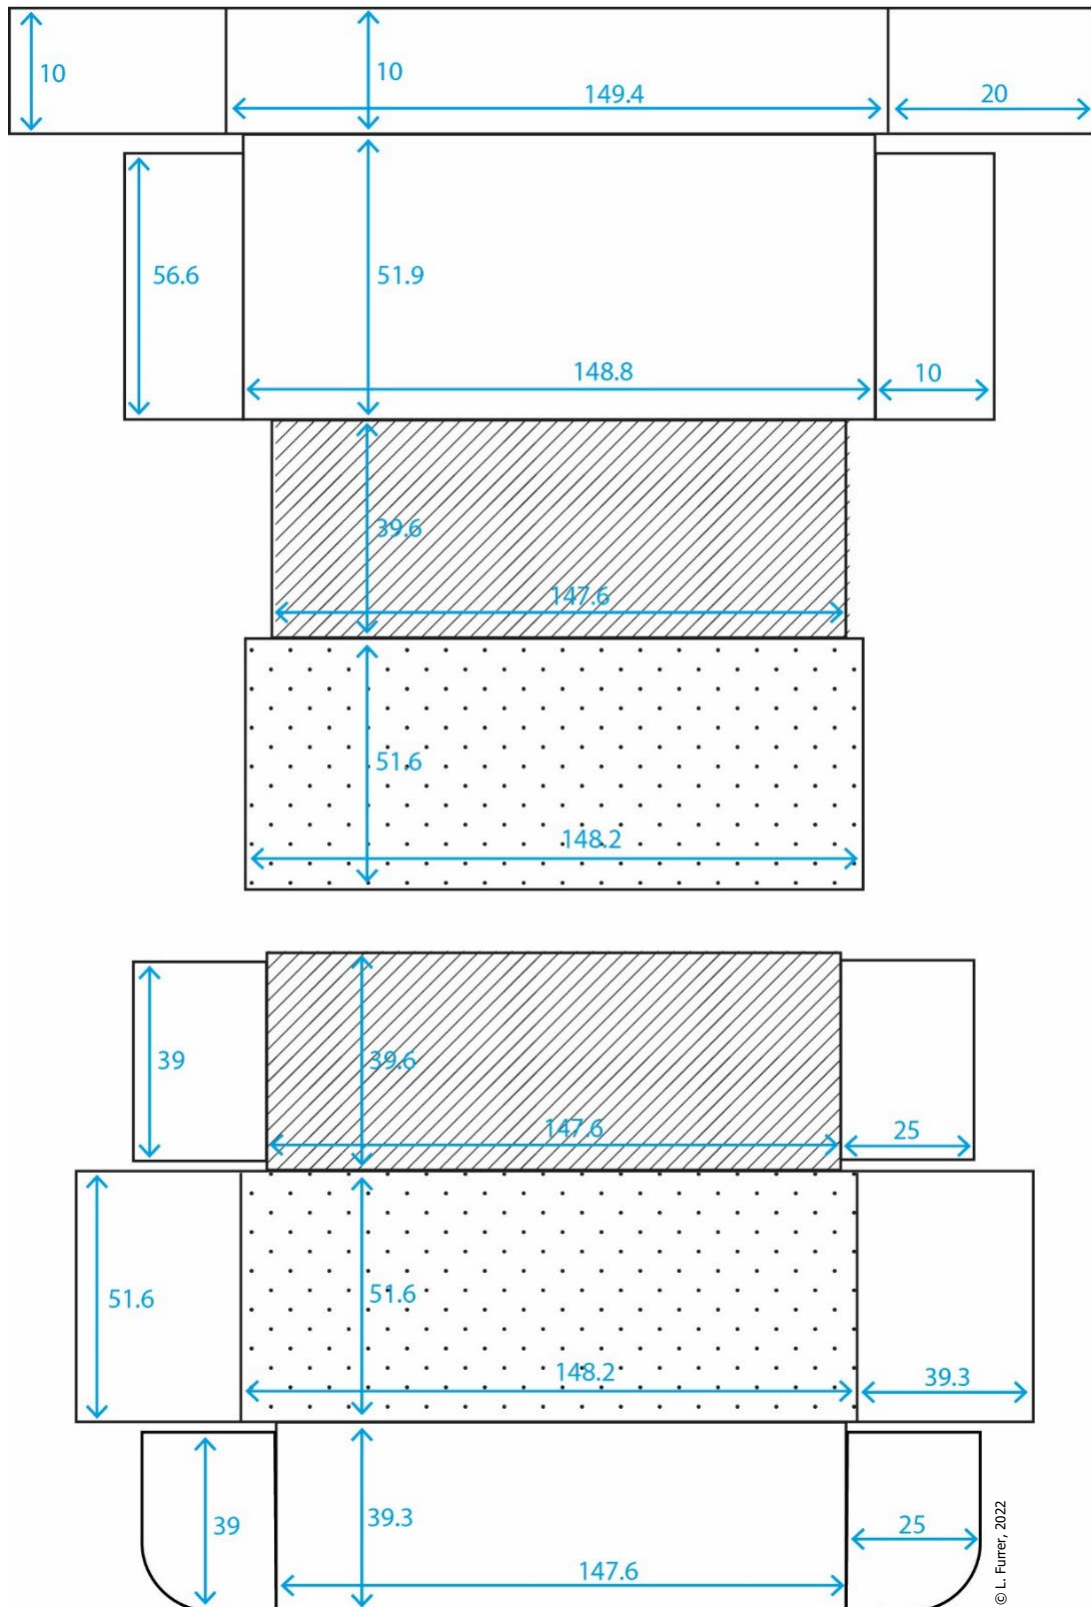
Plan der Schachtel (Einheit: cm). Oben: Deckelteil. Unten: Bodenteil. Gepunktete Flächen: Boden. Schraffierte Flächen: Rückwand. Der Deckelteil wird ausserhalb des Bodenteils mit Drucknieten angebracht.
